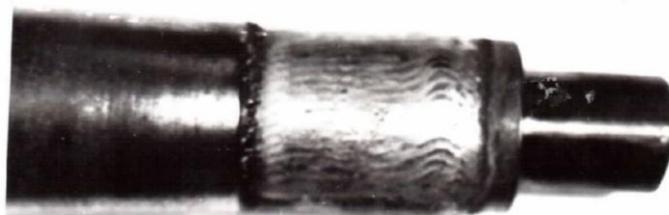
Общий вид наплавляемой поверхности шкворня по диаметру 39мм.
